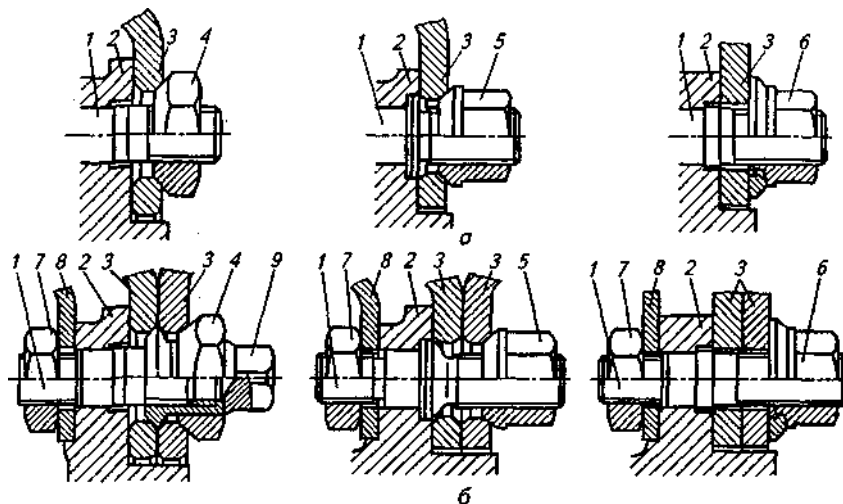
Крепление дисковых колес грузовых автомобилей: *а* — одинарных; *б* — сдвоенных; 1 — шпилька; 2 — ступица; 3 — диск; 4 — гайка крепления наружного диска; 5 — гайка типа ДИН; 6 — гайка с завальцованной шайбой; 7 — гайка крепления тормозного барабана; 8 — тормозной барабан; 9 — гайка крепления внутреннего диска
